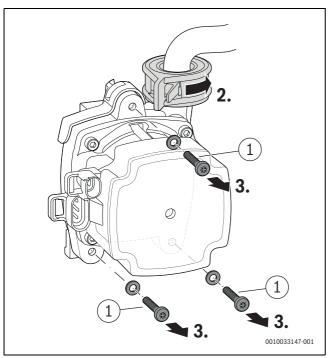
Déverrouiller la pompe de chaudière et retirer les vis
